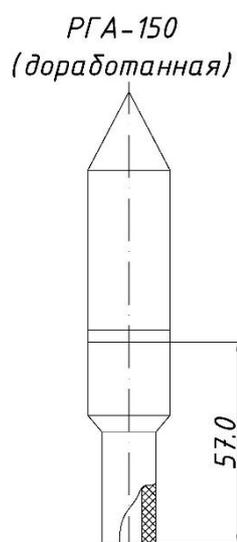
Эскиз конструкции сопла для горелки РГА-150
